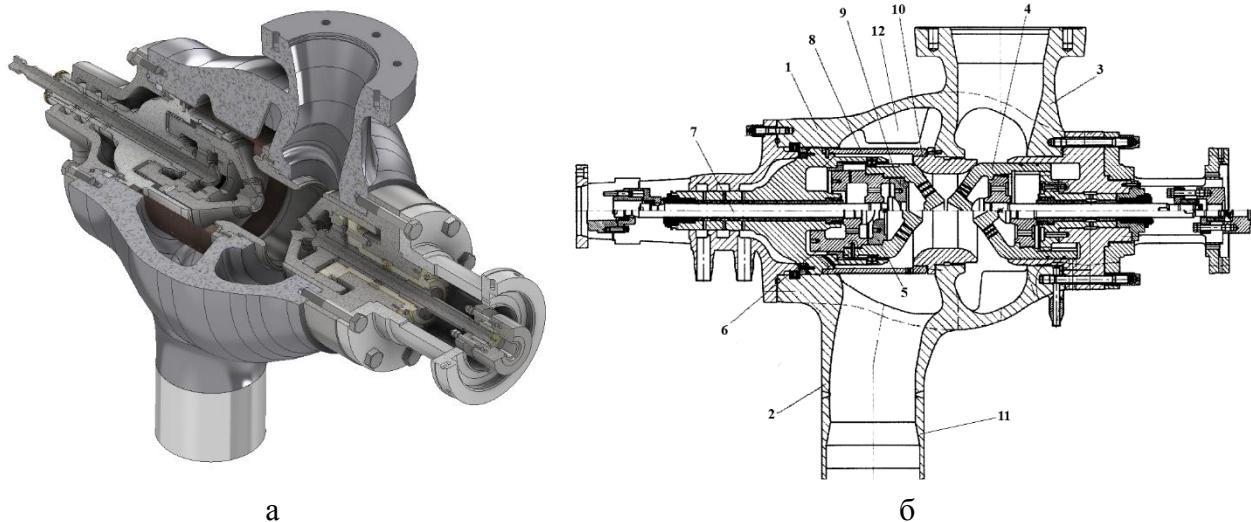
Стопорно-регулирующий клапан: а – 3D модель стопорно-регулирующего клапана, б – продольный разрез проточной части регулирующего клапана: 1 – корпус, 2 – входной патрубок, 3 – выходной патрубок, 4 – стопорный клапан, 5 – седло разгрузочного клапана, 6 – гайка, 7 – шток разгрузочного клапана, 8 – защитная сетка, 9 – регулирующий клапан, 10 – седло, 11 – опорная втулка, 12 – противовихревое ребро
